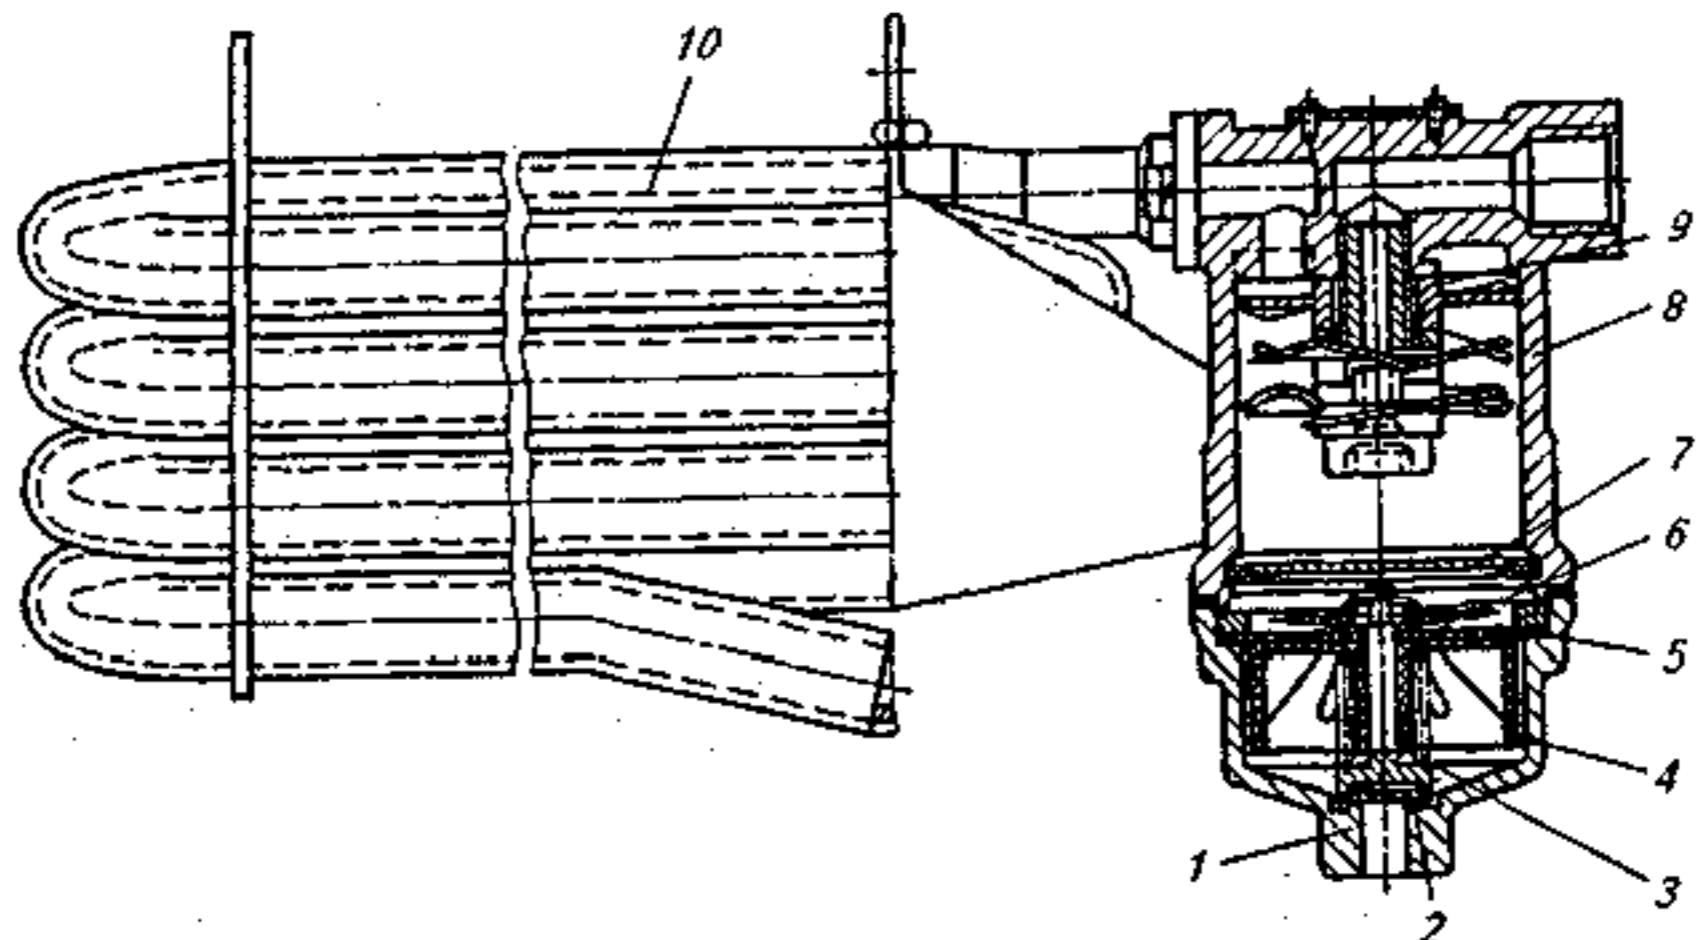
Влагоотделитель: 1 — корпус конденсатосборника; 2— нижний клапан; 3 — пружина; 4— поршень; 5 — диафрагма; 6—верхний клапан; 7—сетка; 8— корпус; 9— лепестковая шайба; 10 —охладитель
